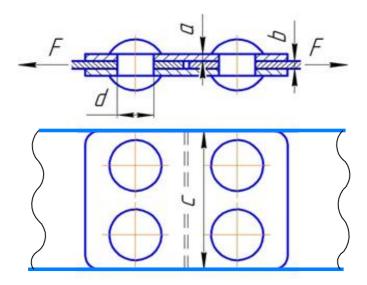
Схема заклёпочного соединения металлических пластин накладками: вверху — продольный разрез соединения, внизу — вид шва сверху
